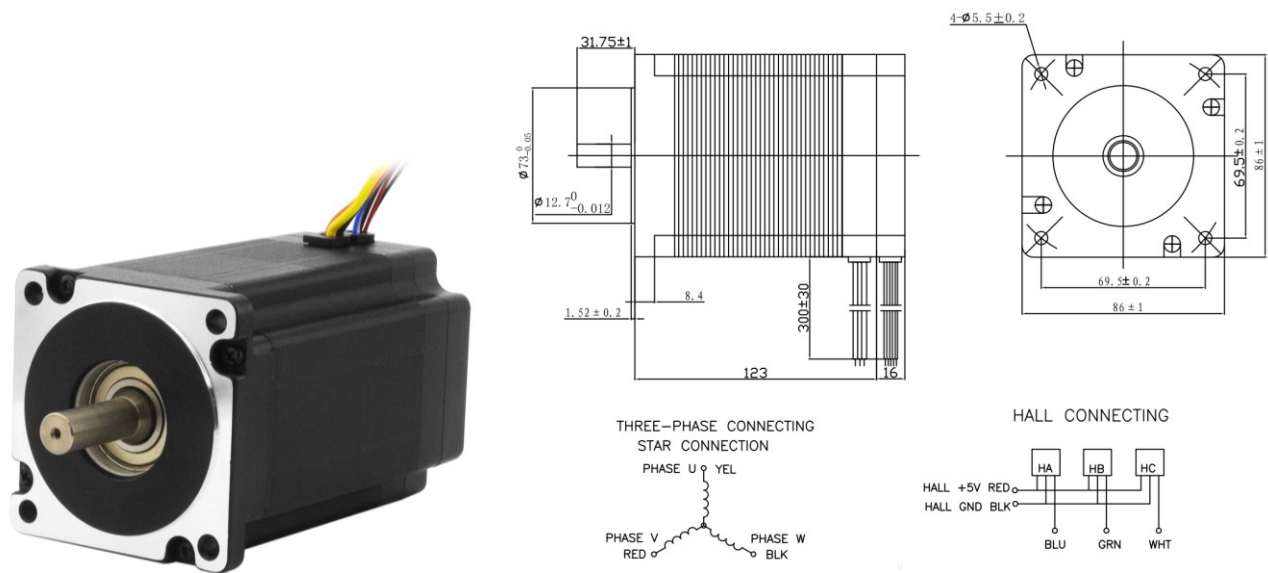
Внешний вид и схематичный чертеж BLDC двигателя
